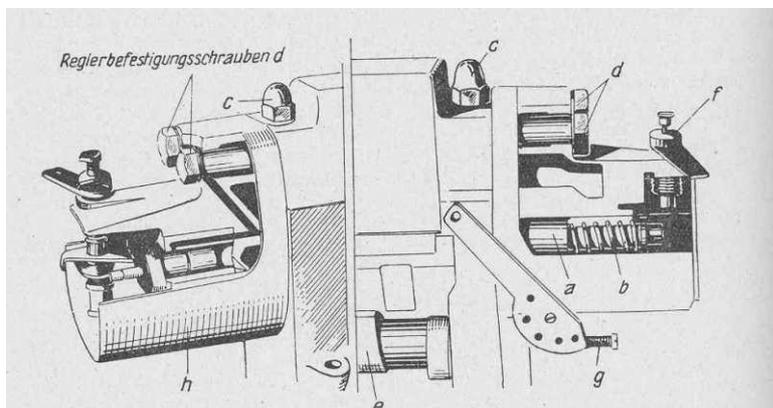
Deutz Regler im Schnitt, a – Kolben, b – Feder, c-Befestigungsmutter des Oberteils, d – Reglerbefestigungsschraube, e – Nockenwelle, f- Reglergehäuse, g – Regelhebel mit Einstellschraube
